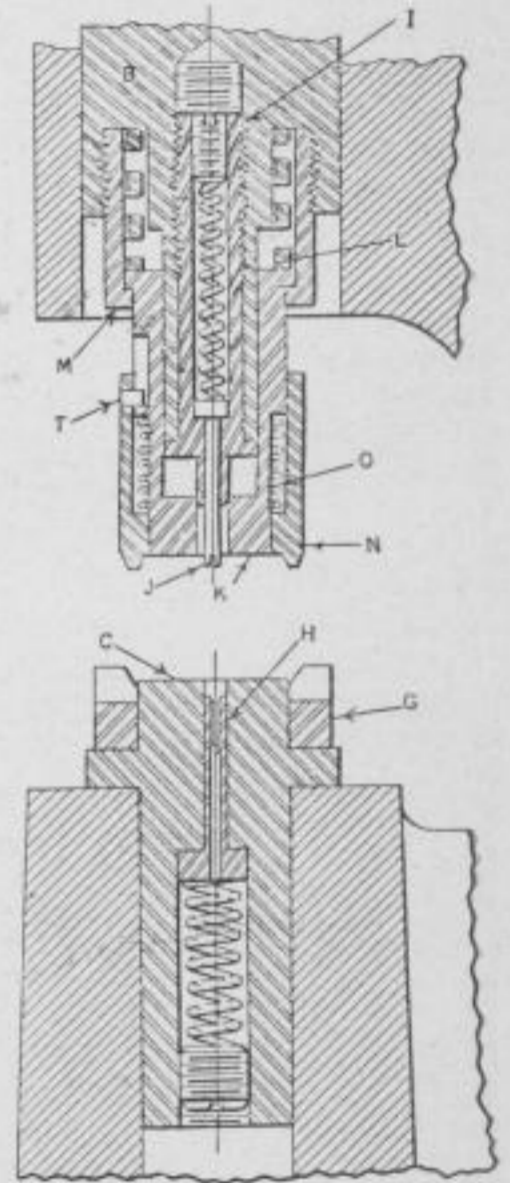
Querschnitt durch die Werkzeuge der Vorrichtung
